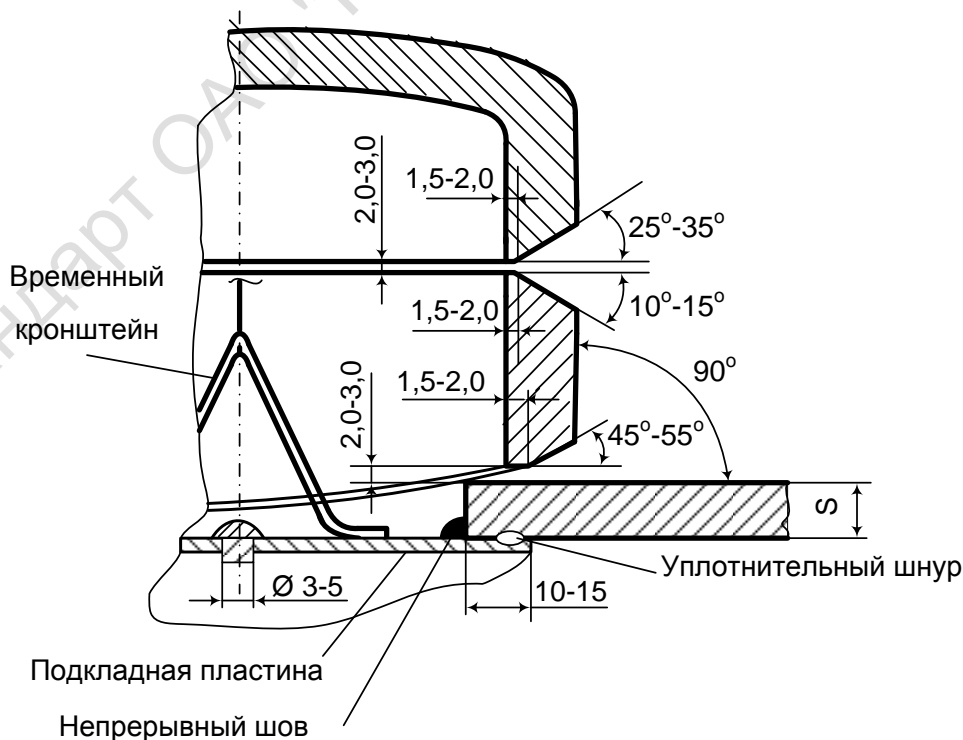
Параметры подготовки кромок патрубка и дна (заглушки)
